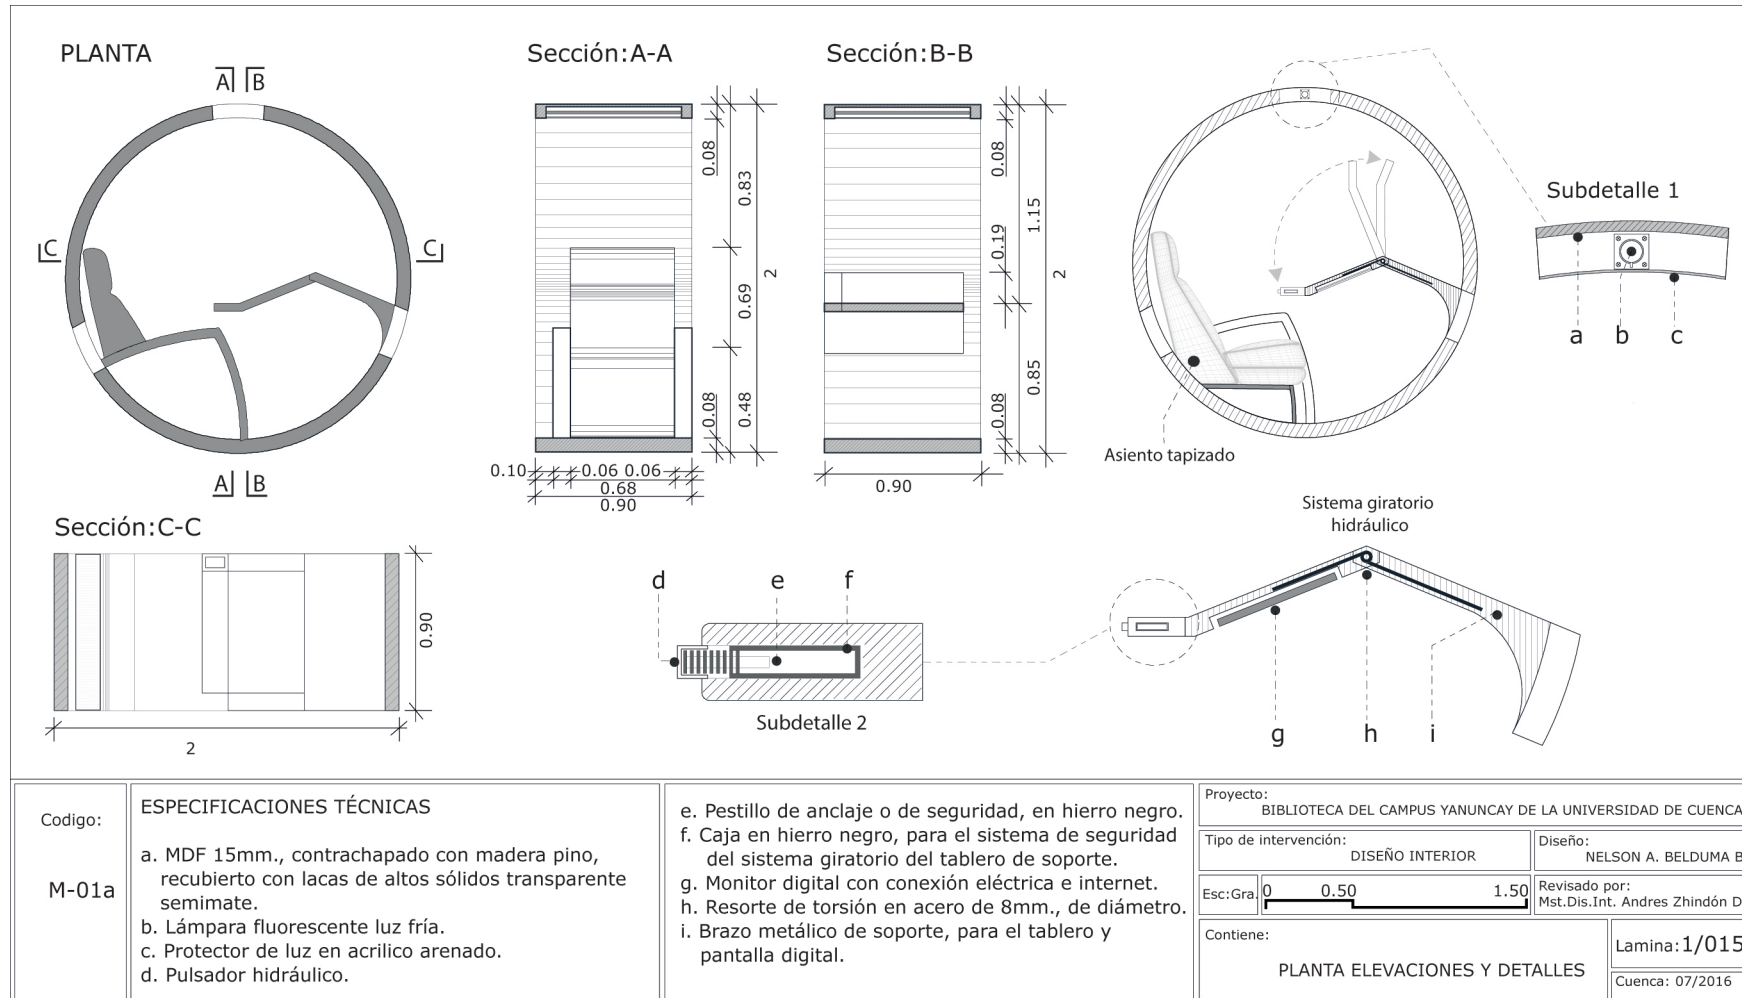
Planta, elevaciones y detalles. Sala de lectura. M-01a.
